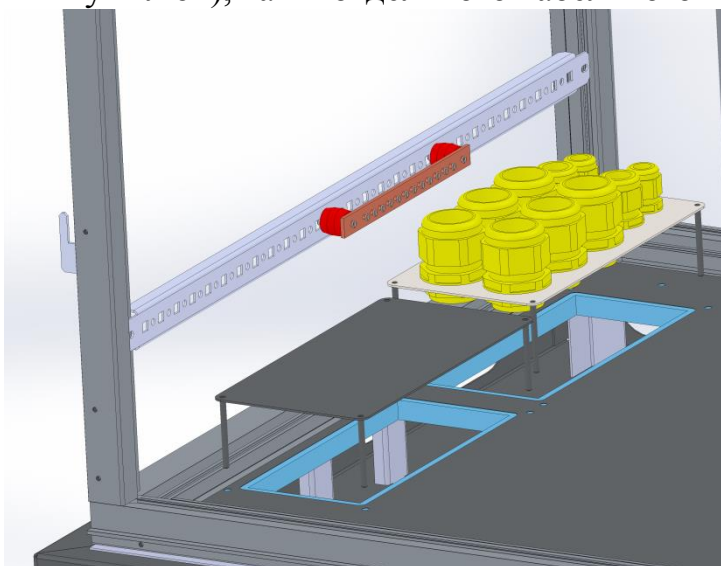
Внешний вид и расположение кабельного люка и шины заземления
